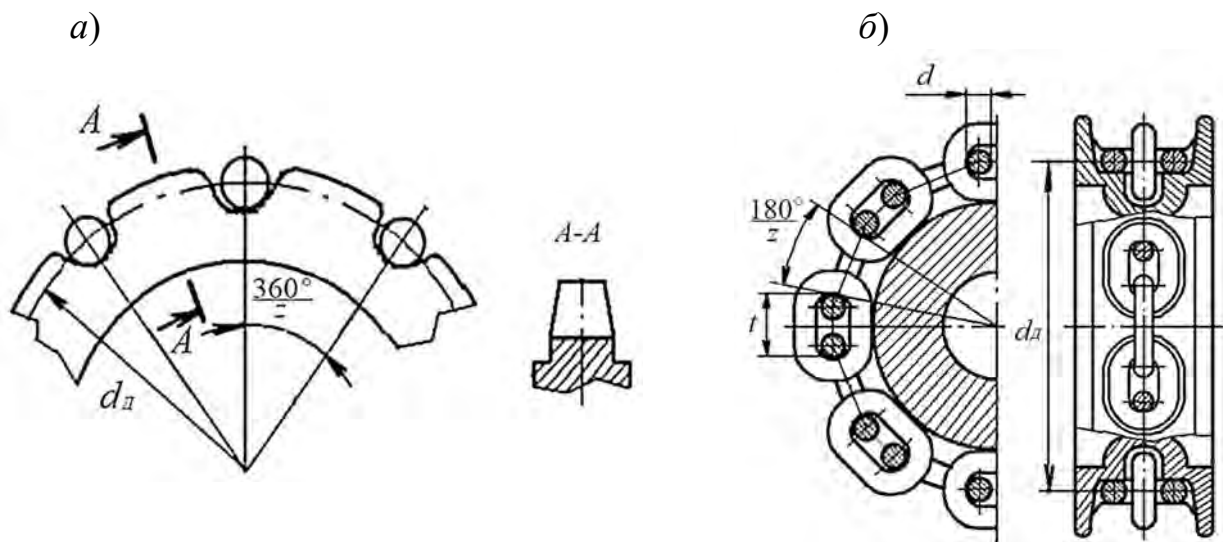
Профиль зуба звездочки: а – для круглозвенной цепи; б – для пластинчатой цепи
